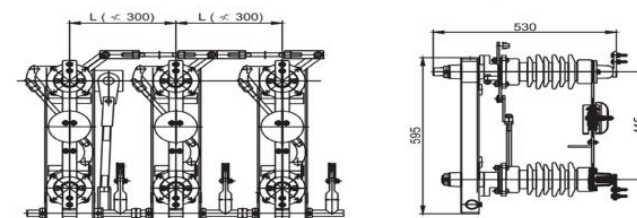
Разъединитель GW4-12D/630 однополюсный
